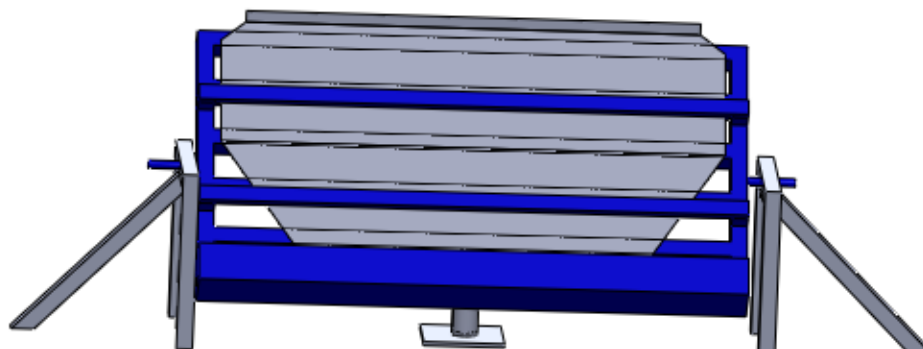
Cordón de soldadura entre frente superior e inferior.
